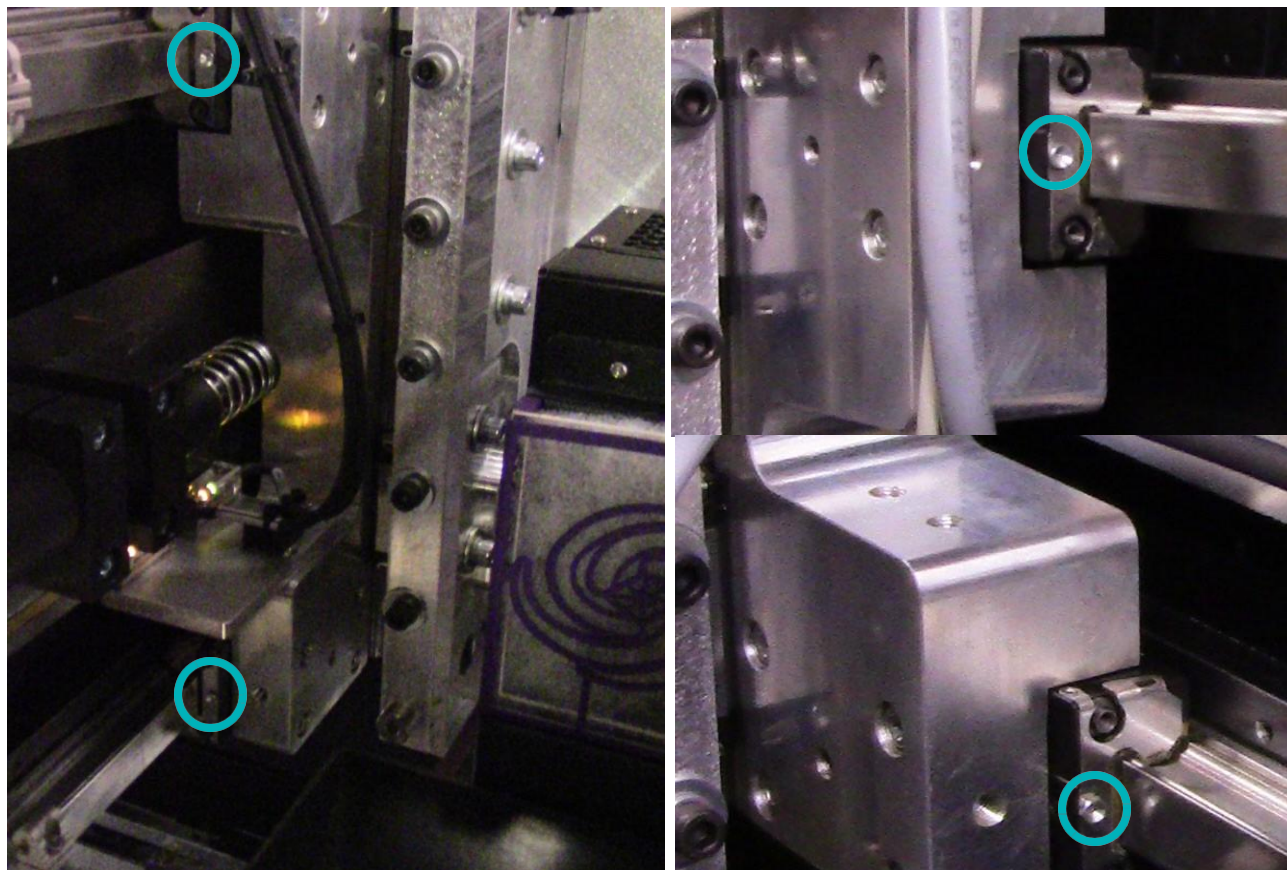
Подшипники каретки, с левой и правой сторон и смазочные отверстия
